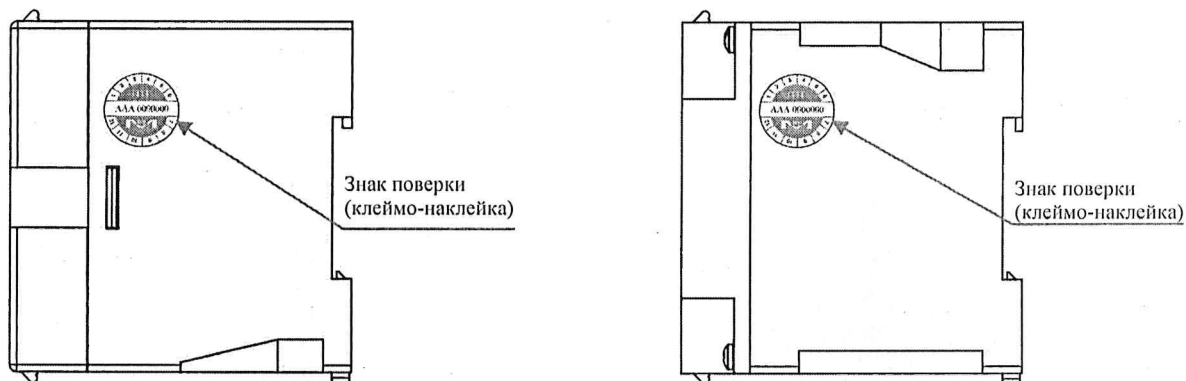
Схема с указанием места для нанесения знака поверки на преобразователи в корпусах М6, М8
